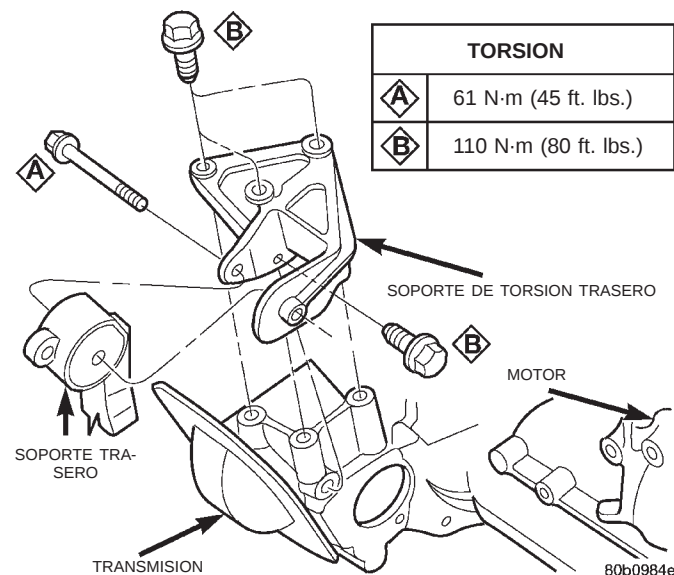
Montaje del motor —Trasero del motor 2.4L
